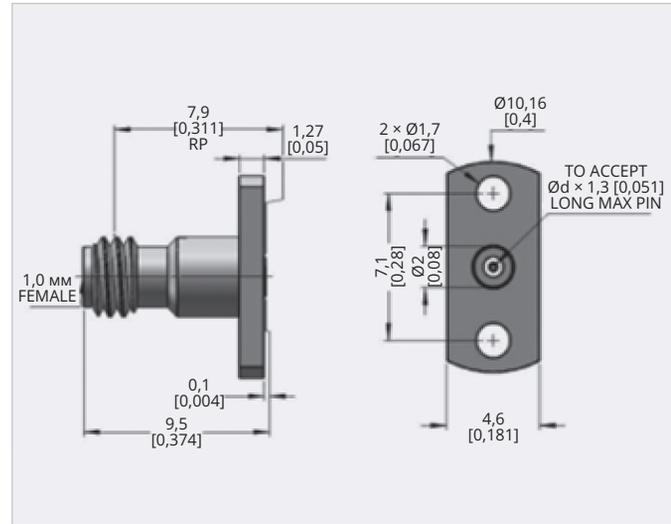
Фланцевый соединитель розетка 1.0 mm – 1.0-KFD807
